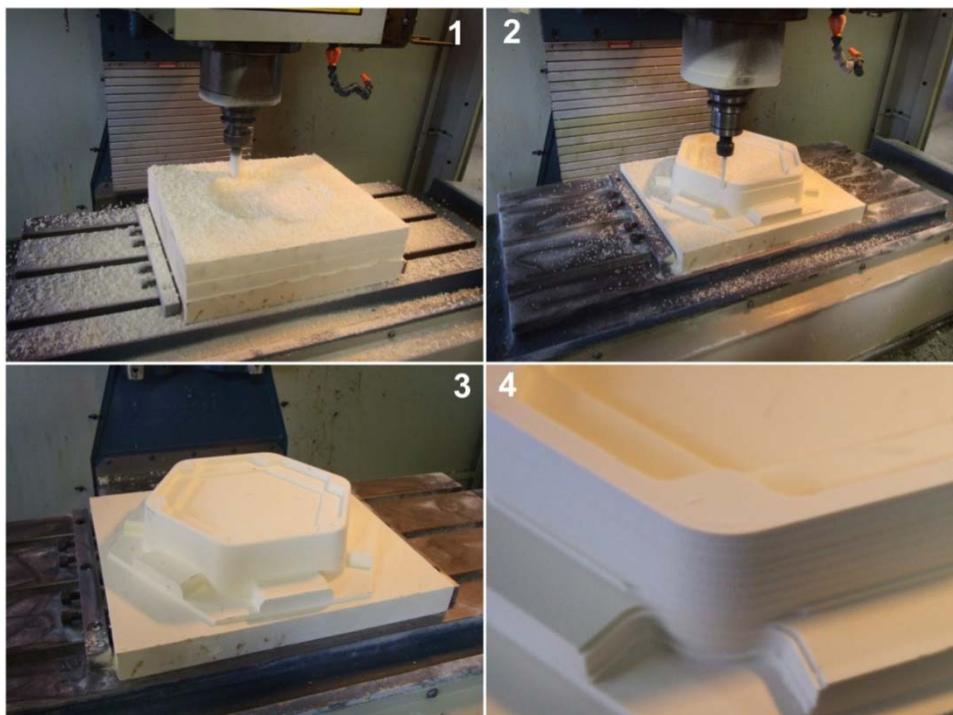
32: Usinagem das matrizes. (1) Entrado do bloco retangular de PU na máquina CNC. (2) Usinagem em andamento. (3) Usinagem finalizada com o pré-molde do corpo. (4) Detalhe da usinagem intermediária.
